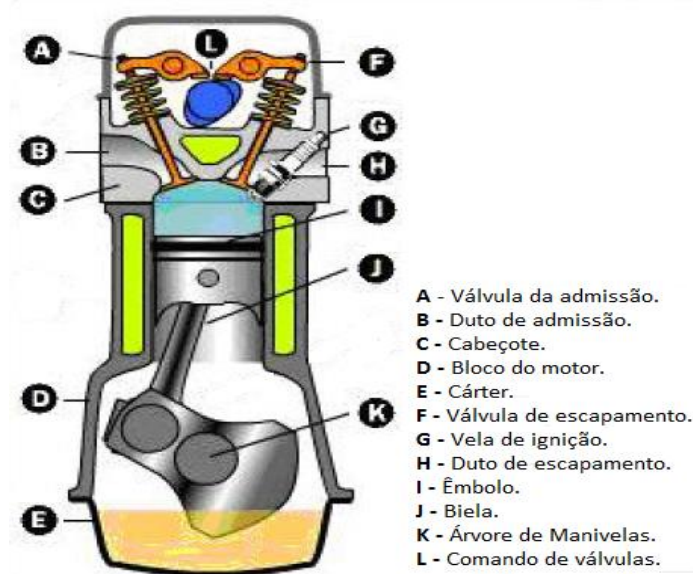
Principais componentes de um motor de combustão interna ciclo Otto (Adaptado de Oliveira, 2009).
